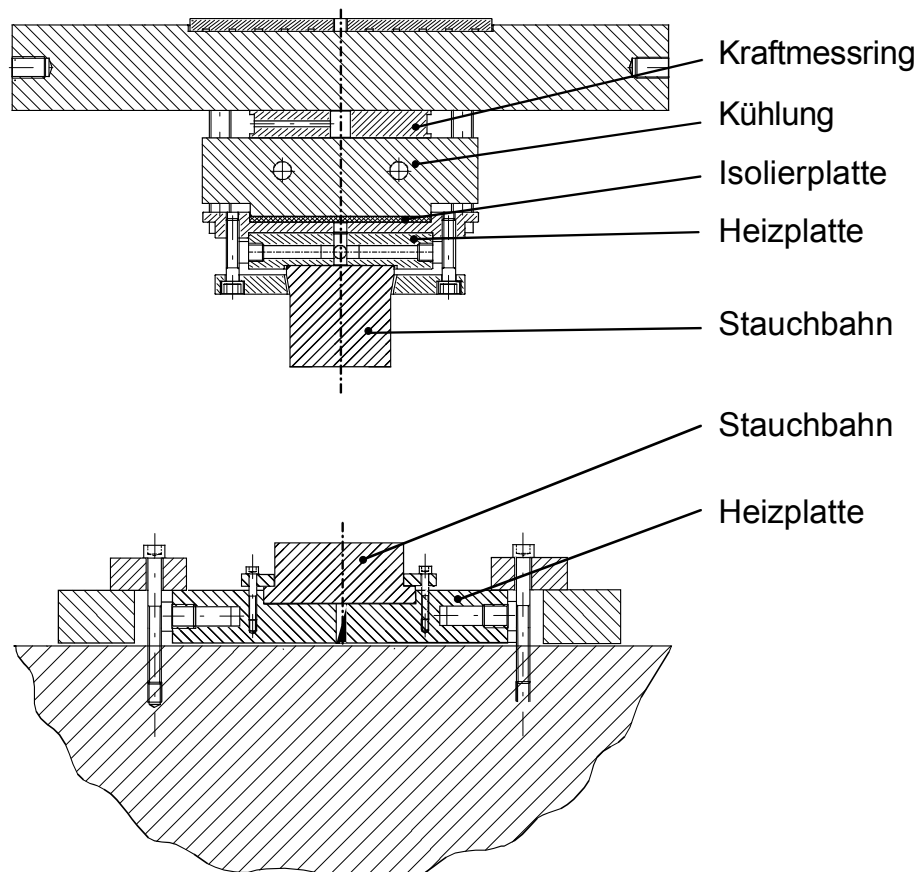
Versuchswerkzeug zur Durchführung von Ringstauchversuchen
